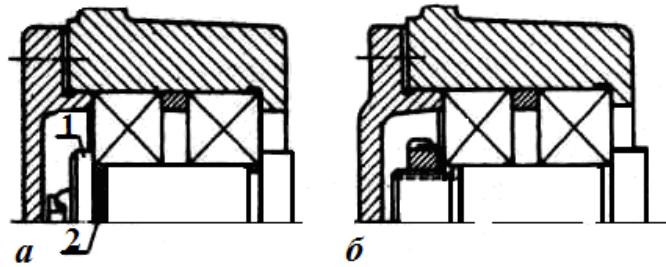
Способы осевого смещения внутренних колец подшипников
